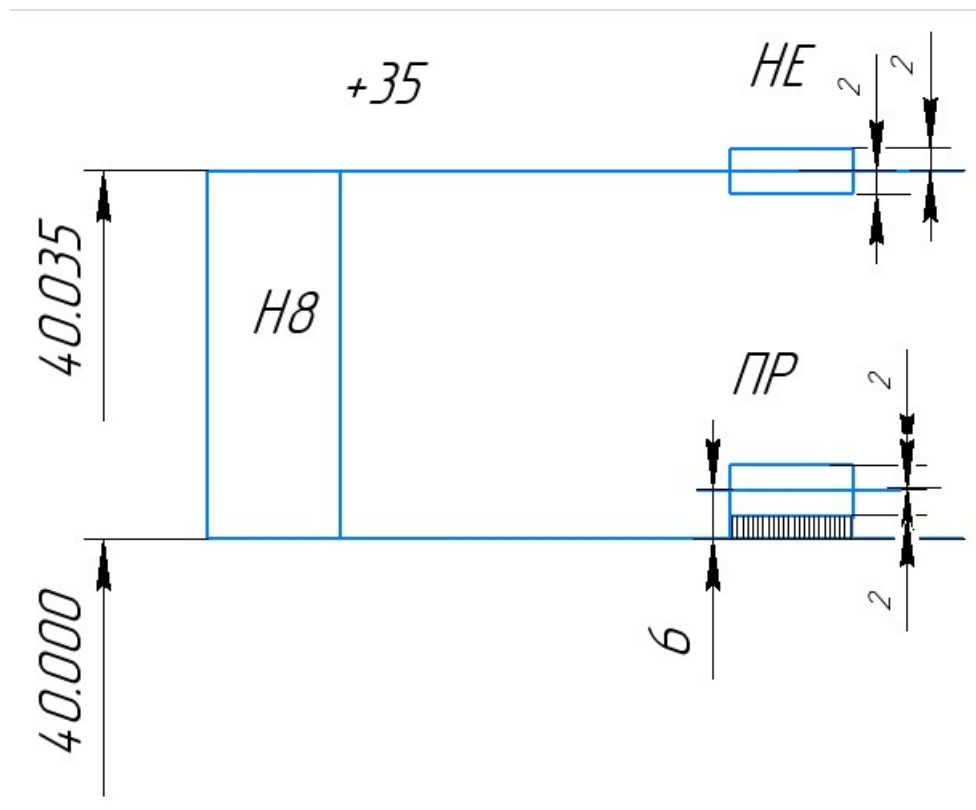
Схема розташування поля допуску калібру пробки D40H8
